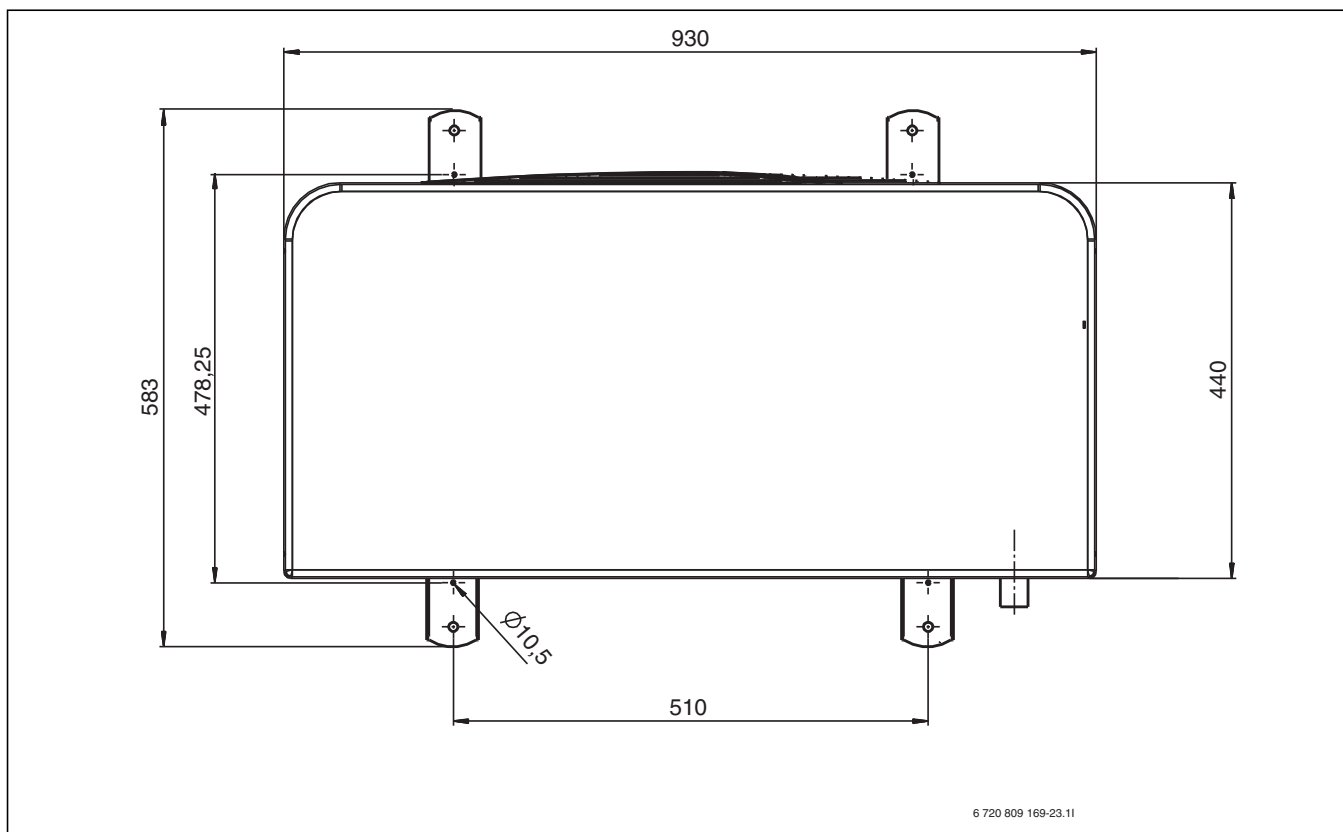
Размеры теплового насоса, верх, типоразмеры 5-9
